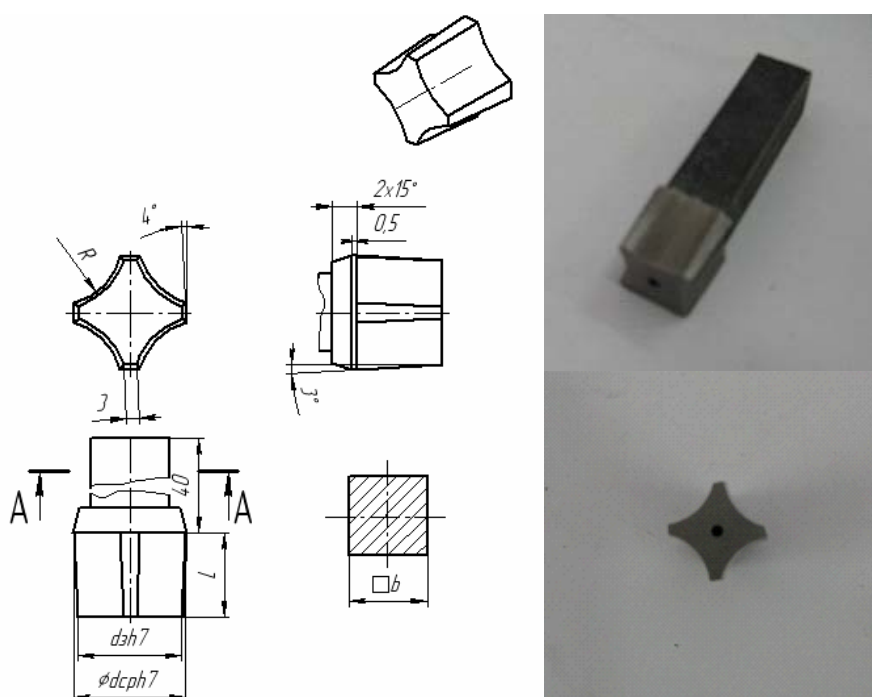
Деформирующий инструмент для глухих отверстий
